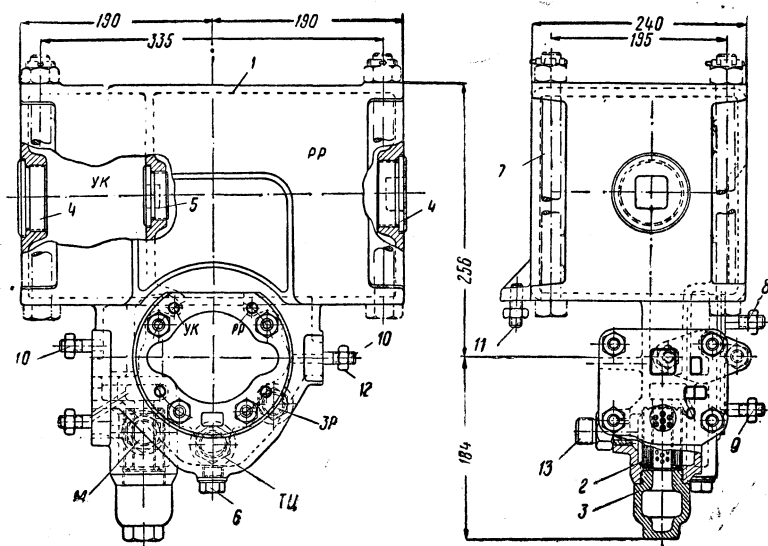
Двухкамерный рабочий резервуар усл. №145
